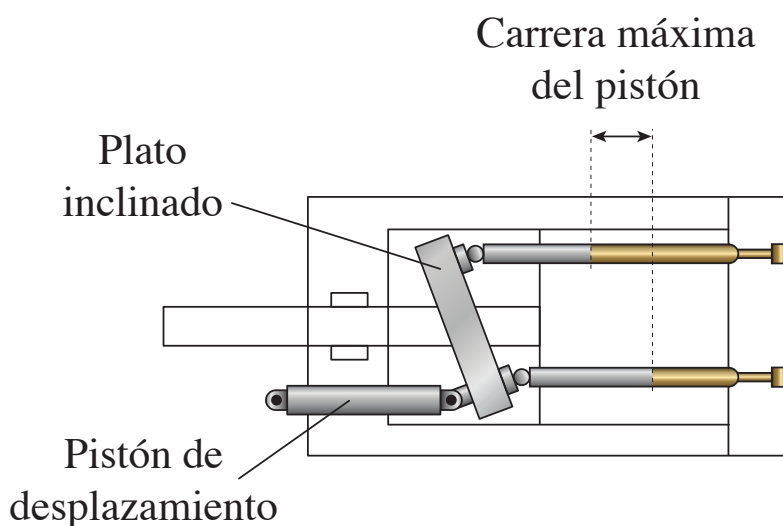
Bomba de pistones de tipo placa inclinada.
